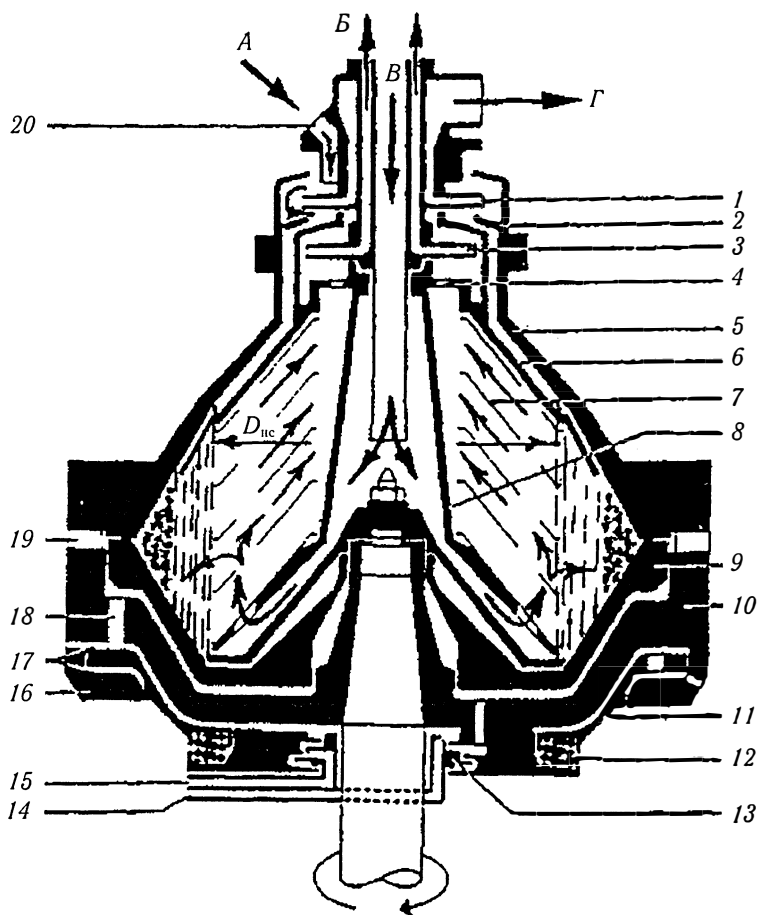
Барабан сепаратора серии WHPX: 1 — напорный диск для удаления отсепарированной воды (по стрелке «Г»), 2 — регулировочная шайба; 3 — напорный диск для удаления очищенного топлива (по стрелке «Б»), 4 — шайба; 5 — колпак барабана; 6 — верхняя (разделительная) тарелка; 7 — пакет тарелок; 8 — тарелкодержатель; 9 — подвижное дно барабана; 10 — корпус барабана; 11 — управляющее кольцо; 12 — пружина; 13 — напорный диск для рабочей воды; 14 — патрубок для подачи «открывающей» воды; 15 — патрубок для подачи «закрывающей» воды; 16 — кольцо; 17 — камера с соплами; 18 — сливной канал; 19 — разгрузочные отверстия; 20 — подача воды для гидравлического затвора и частичной выгрузки (по стрелке «А»)
